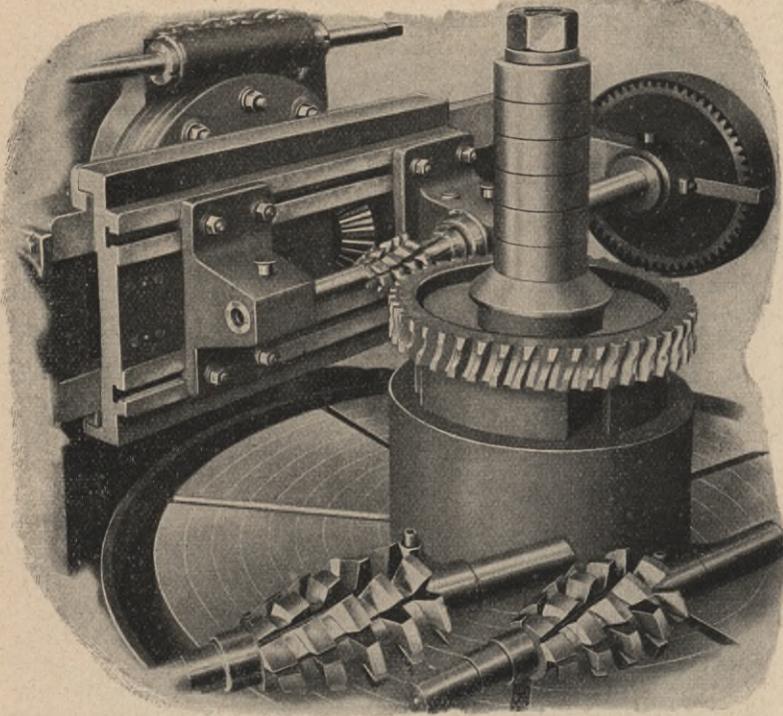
Maschine mit Quervorschubeinrichtung beim Fräsen eines Schneckenrades mit angespitztem Fräser
